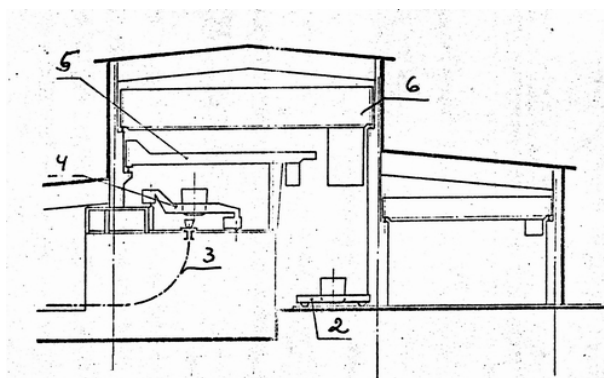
Линейное расположение МНЛЗ с разливкой стали с подвижных стенов. Разрез: 1 — конвертер, 2 — сталевозная тележка, 3 — МНЛЗ, 4 — сталеразливочный подвижной стенд, 5 — полупортальный кран, 6 — мостовой разливочный кран
